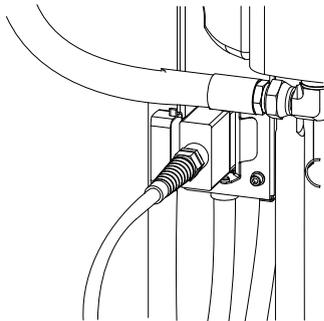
Collegamento del flessibile alla scatola di giunzione
